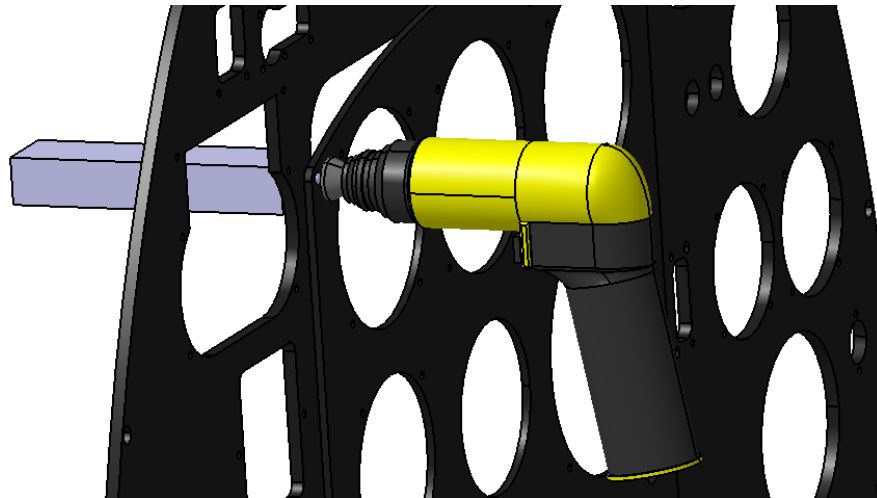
Panel de instrumentos: Remachado indirecto entre partes 1 y 2
